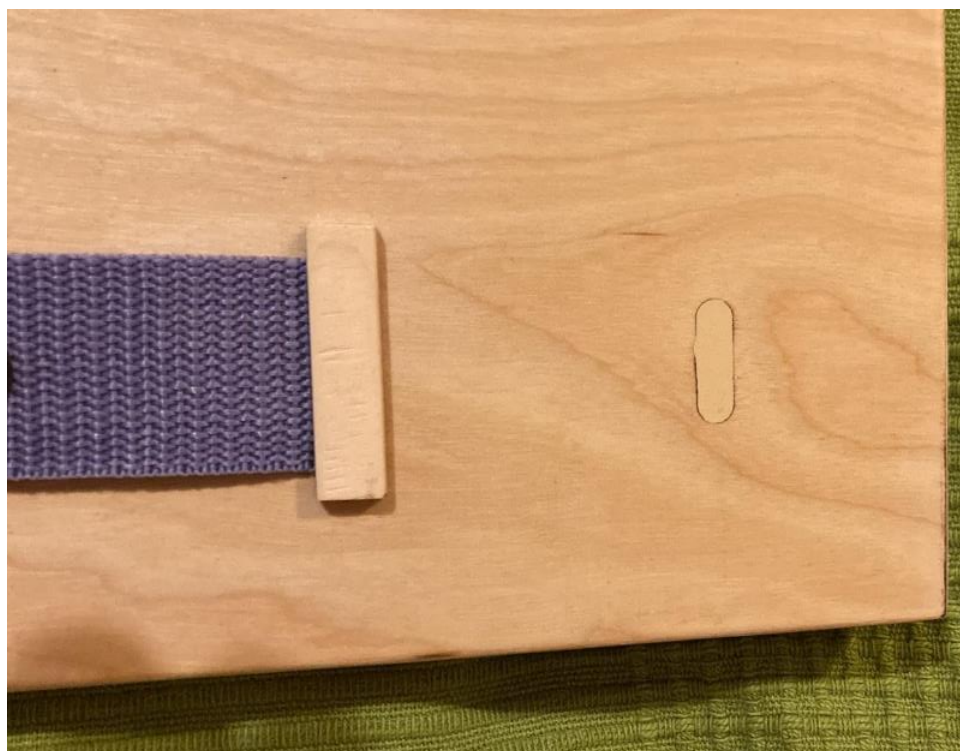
Mierzenie zamontowanej przewodnicy i elementów ruchomych.
